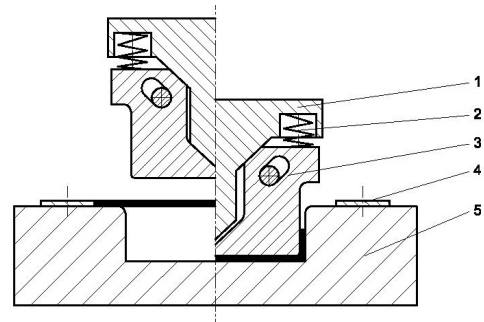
U-Biegewerkzeug - Prägedruck
